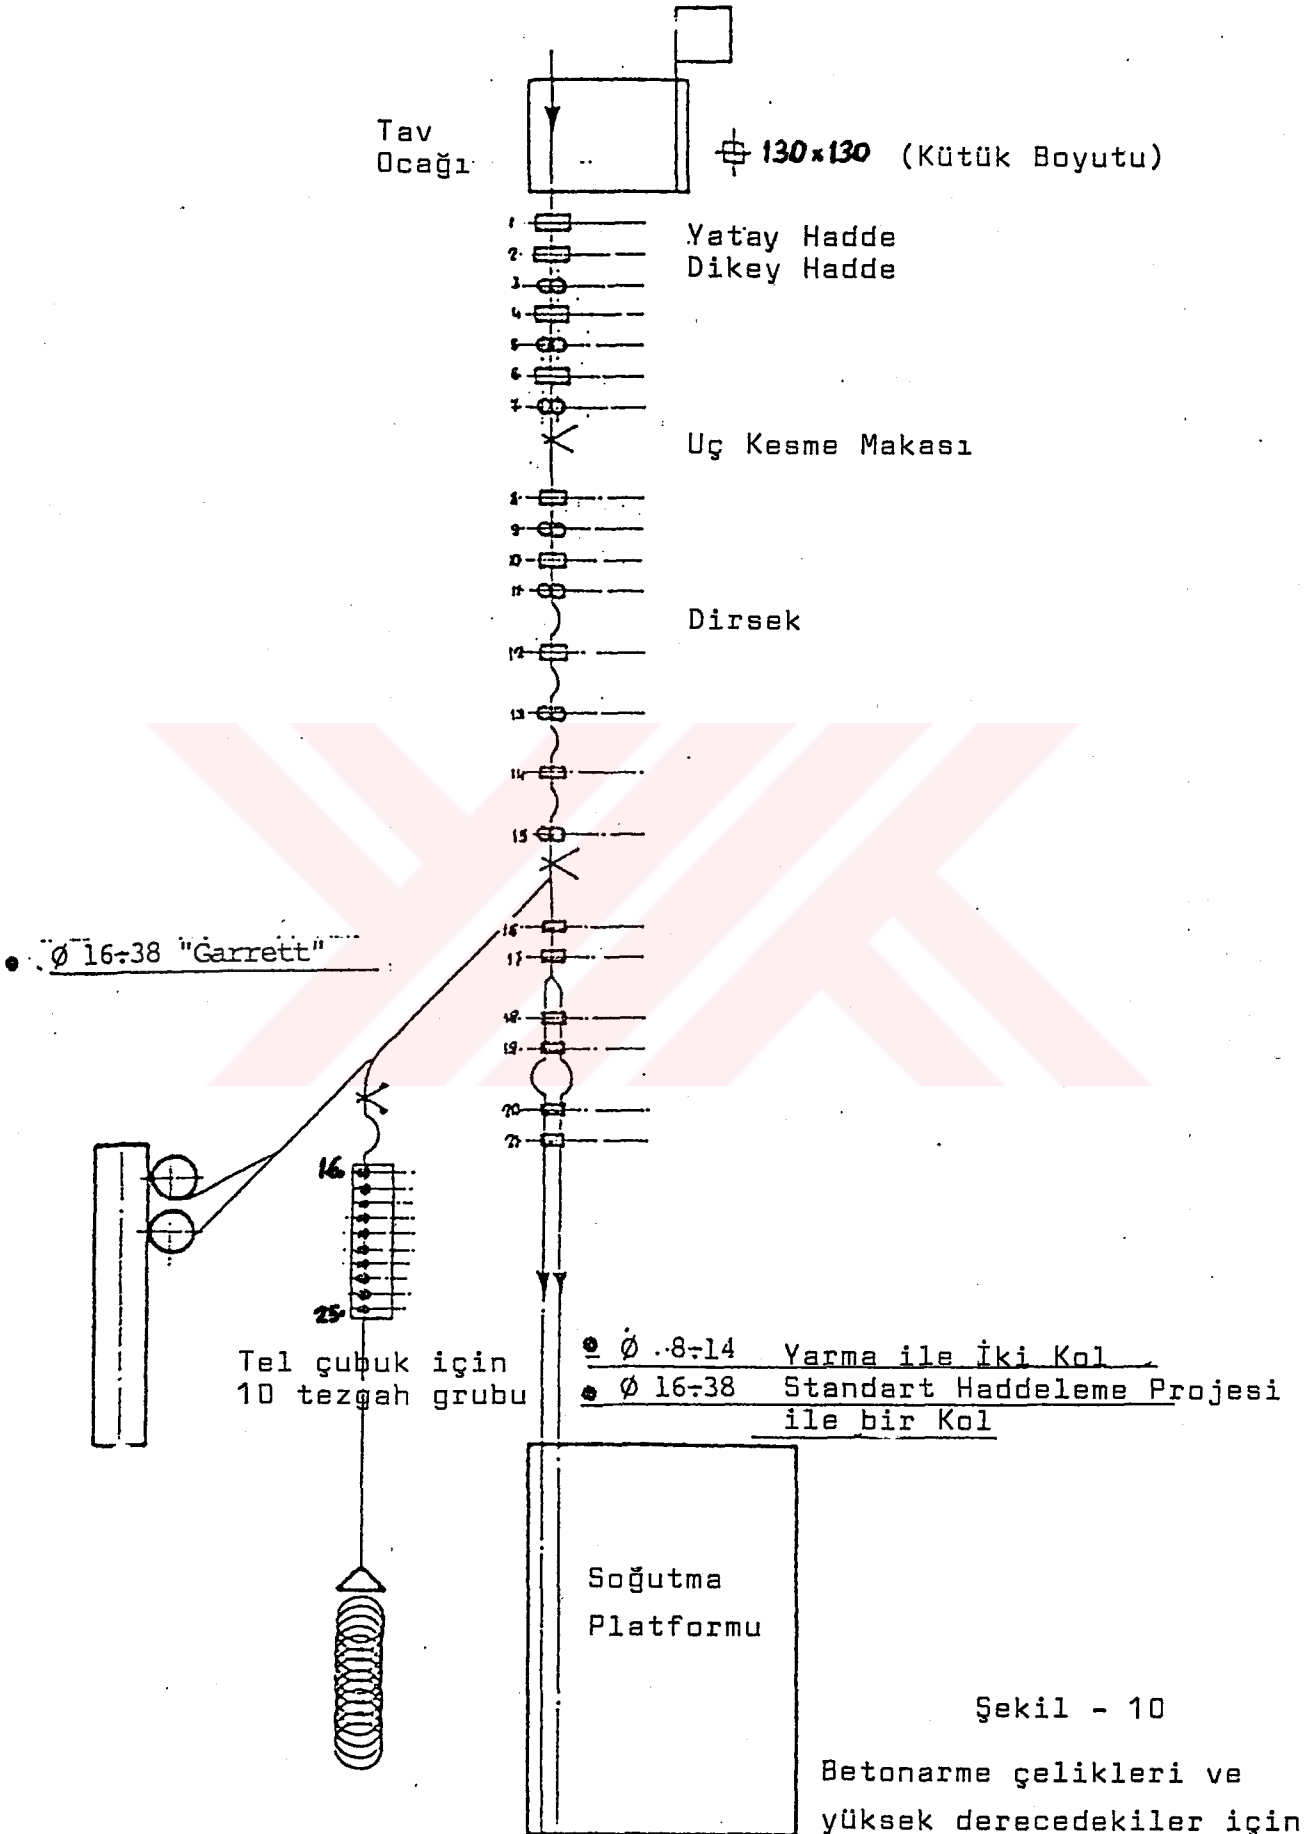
'da gösterilen fabrika planı bir fabrikada yapılan üretimi örneklerle açıklar.
